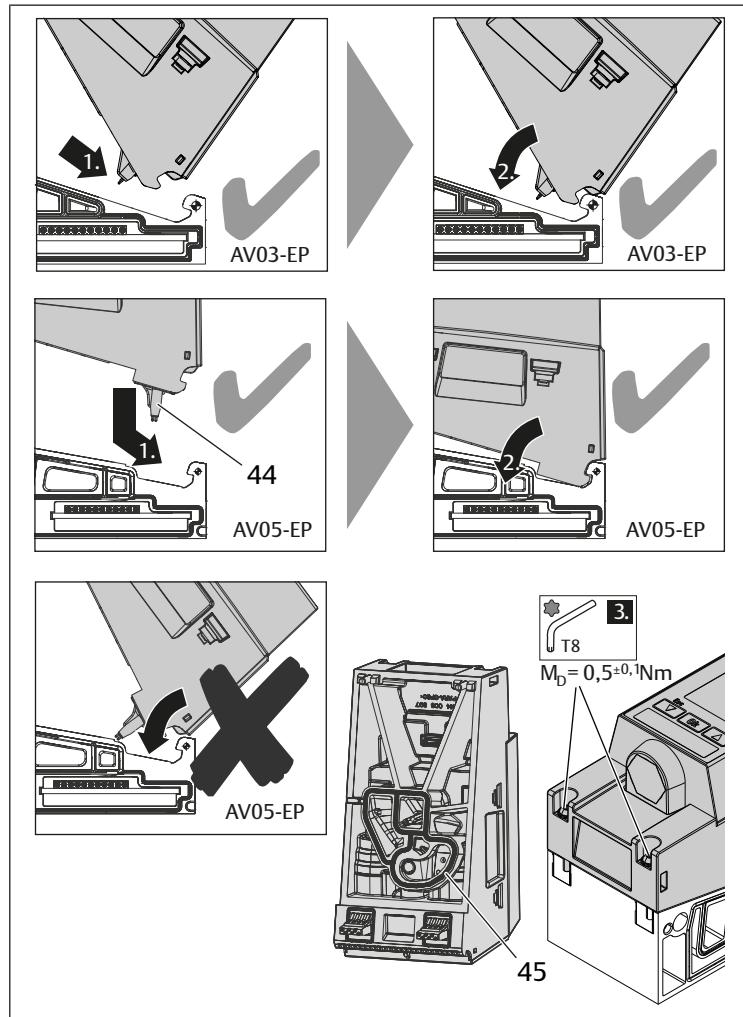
Montaje de la válvula reguladora de presión AV-EP en la placa base
